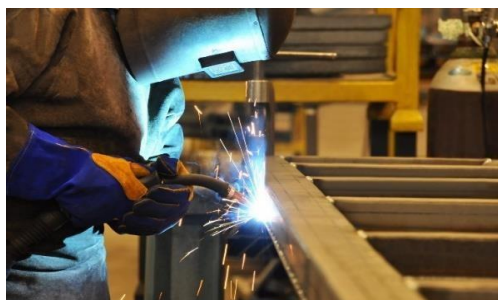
Soldadura MIG/MAG (Aventa, 2016).
